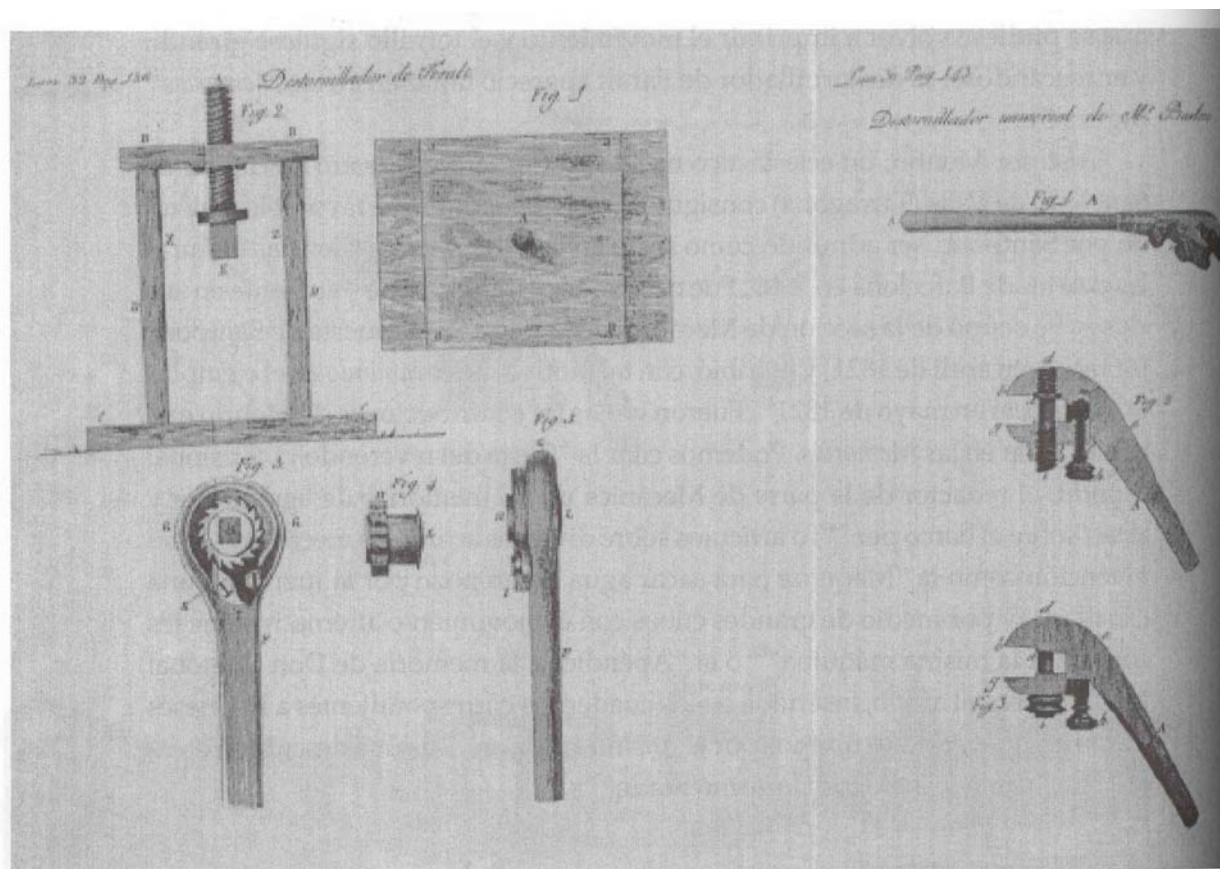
Destornillador universal inventado por Barlow (derecha) y destornillador mejorado inventado por Faralt (izquierda) (MAA, septiembre y diciembre 1816)
